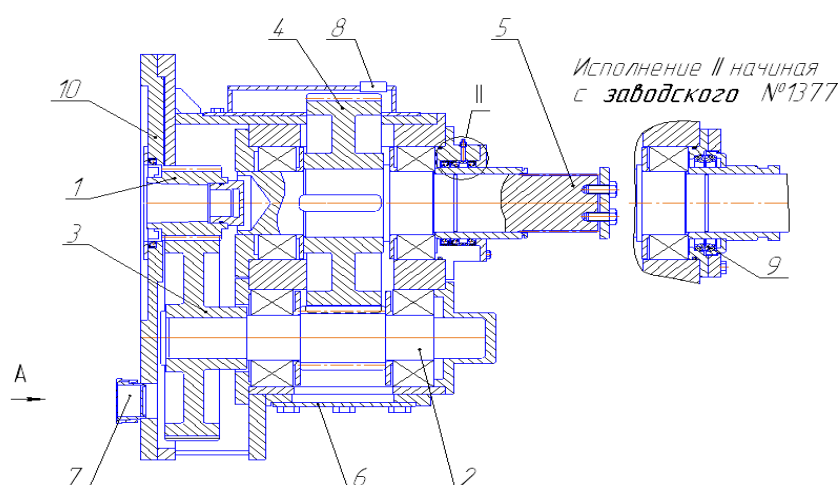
Редуктор: 1 - ведущая шестерня; 2 - вал-шестерня; 3 - колесо; 4 - колесо; 5 - вал; 6 - крышка; 7 - сапун; 8 - сливная заглушка; 9 – уплотнение торцевое TLDOA 1830; 10 – фланец
